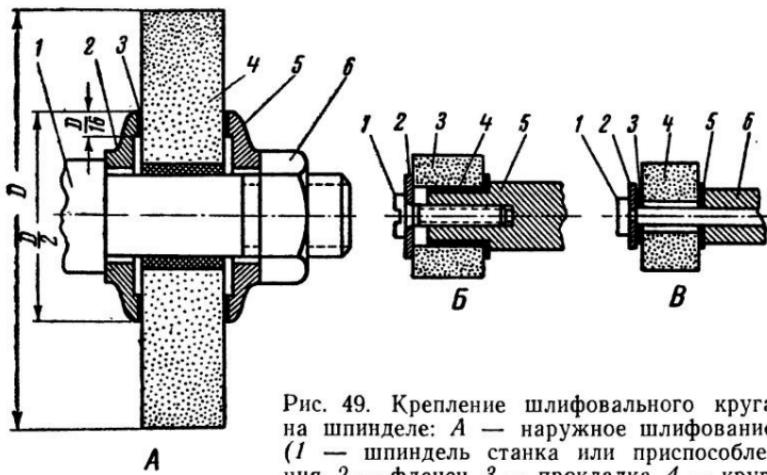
Крепление шлифовального круга на шпинделе: *A* — наружное шлифование (1 — шпиндель станка или приспособления, 2 — фланец, 3 — прокладка, 4 — круг, 5 — шайба, 6 — гайка); *B* — внутреннее шлифование (1 — крепежный винт, 2 — шайба, 3 — круг, 4 — втулка, 5 — шпиндель); *C* — внутреннее шлифование (1 — затяжной шомпол — крепится к противоположному торцу пустотелого шпинделя, 2 — шайба, 3 — прокладка, 4 — круг, 5 — прокладка, 6 — шпиндель).
